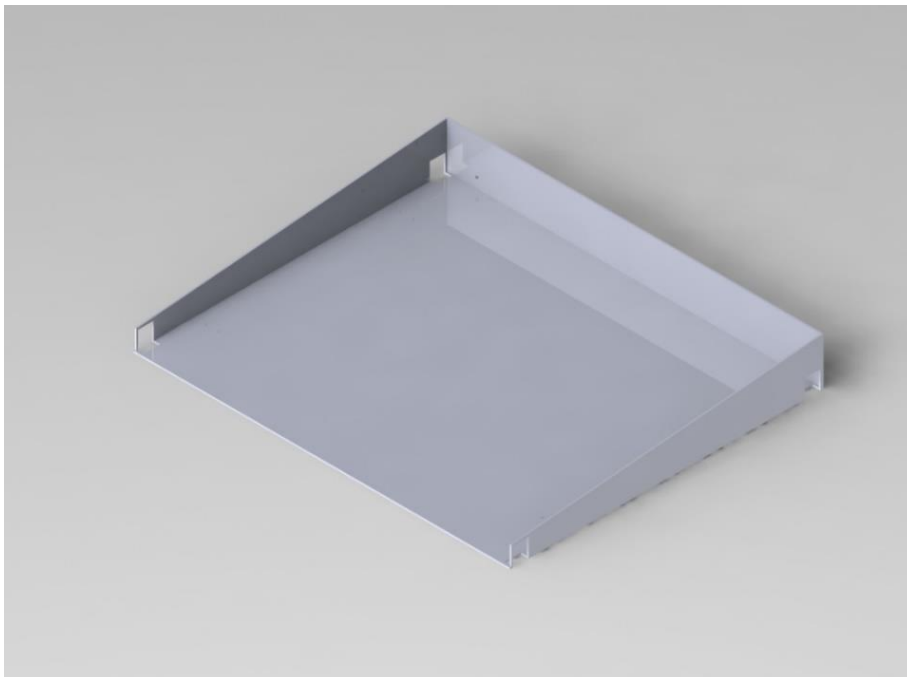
Ensamblaje subconjunto 1.4. Soldadura 1.
